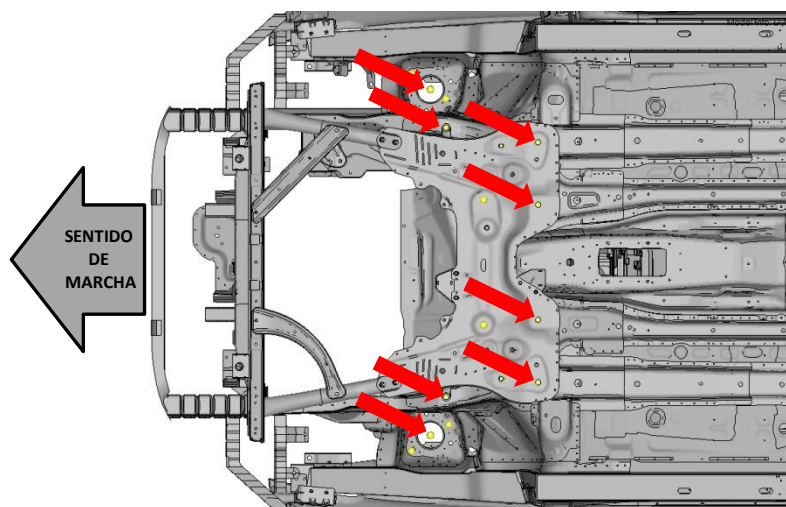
Pavimento do veículo - Pontos de medição das funções de sensibilidade da suspensão dianteira.
